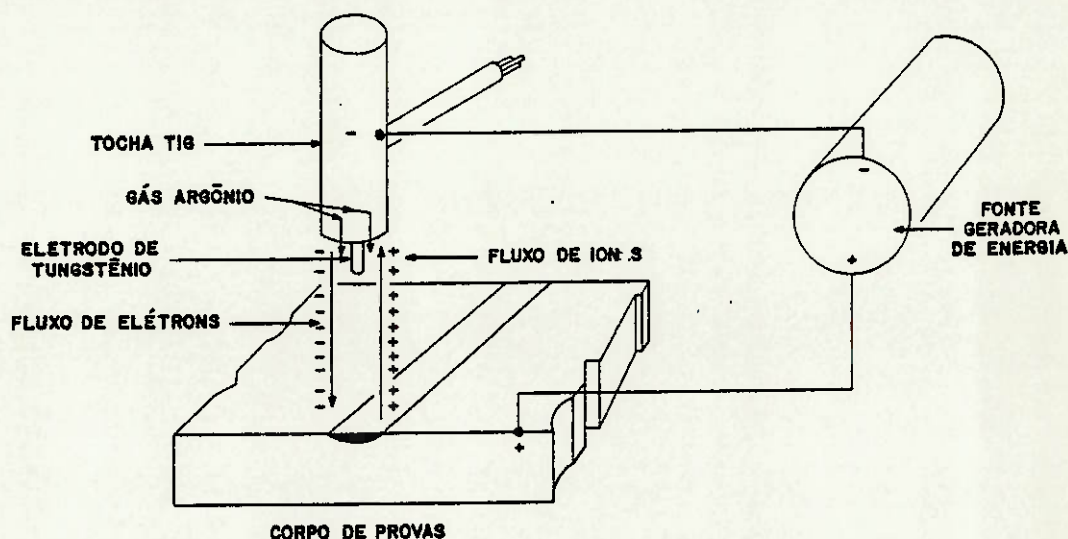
PROCESSO DE SOLDAGEM DCSP-TIG
